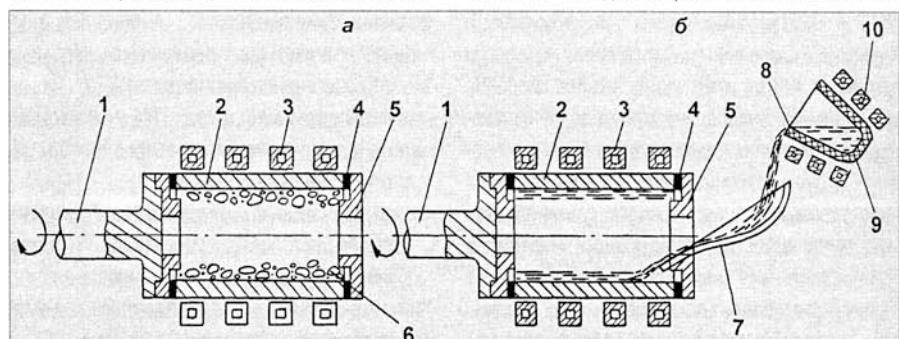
Принципиальные схемы индукционной наплавки центробежной заливкой с использованием твердого (а) и расплавленного (б) присадочного материала: 1 – шпиндель центробежной машины; 2 – наплавляемая деталь; 3 – индуктор; 4 – прокладка; 5 – крышка; 6 – шихта; 7 – керамический желоб; 8 – расплавленный металл; 9 – тигель; 10 – индуктор плавильного агрегата
